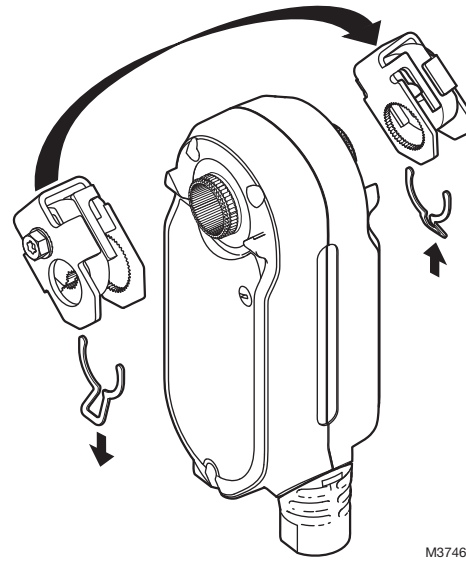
Montaje del acoplamiento del eje en el extremo opuesto del actuador.
